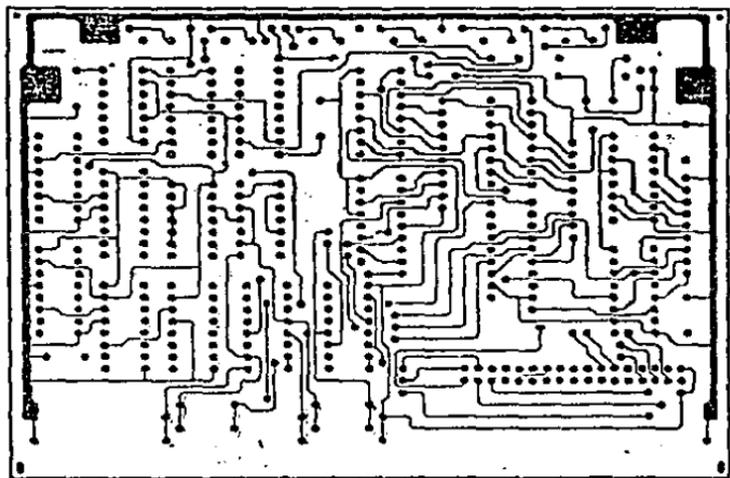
Circuito impreso "principal" lado de soldadura.
